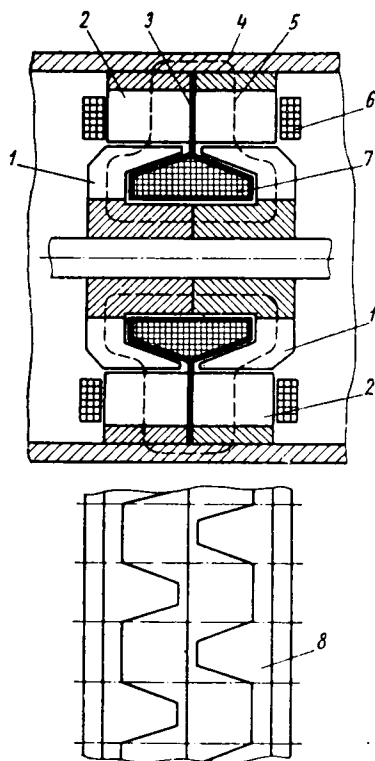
Эскиз магнитной цепи двухпакетного генератора с укороченными когтями ротора:
